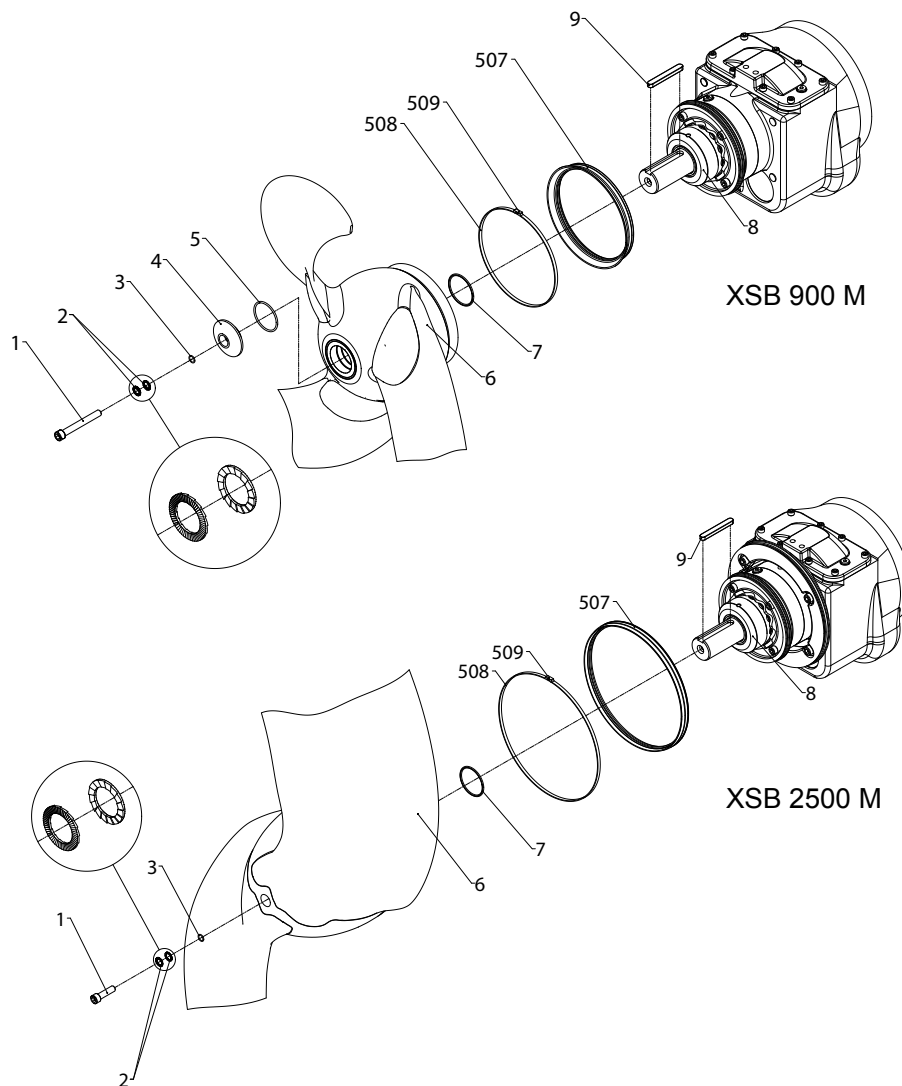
Propellermontage/-demontage XSB 900; XSB 2500
